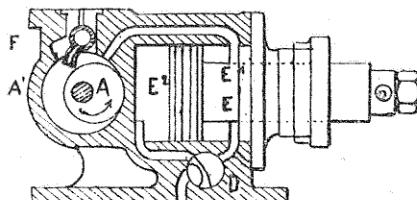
Machine Wilkinson-Sellers, à triple expansion.
